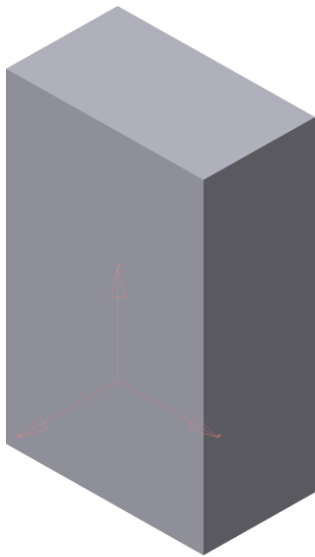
Пачка (отримана із заготовки рис.1.1)
